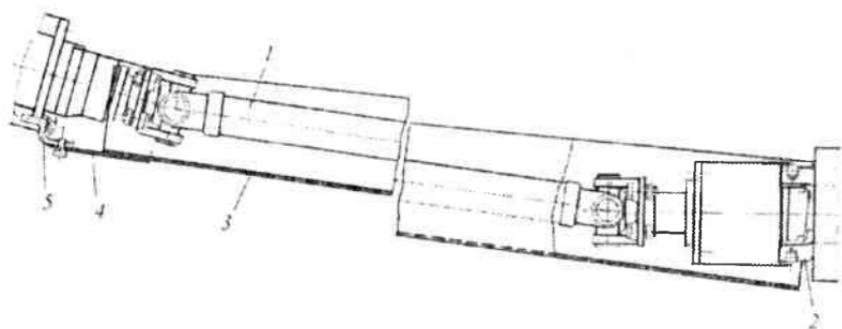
Карданный привод: 1 – вал карданный; 2, 5 – скоба; 3 – кожух; 4 – опора
